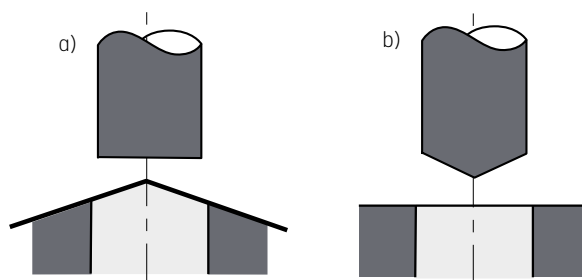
Herramientas achaflanadas para a) troquelado y b) punzonado.
